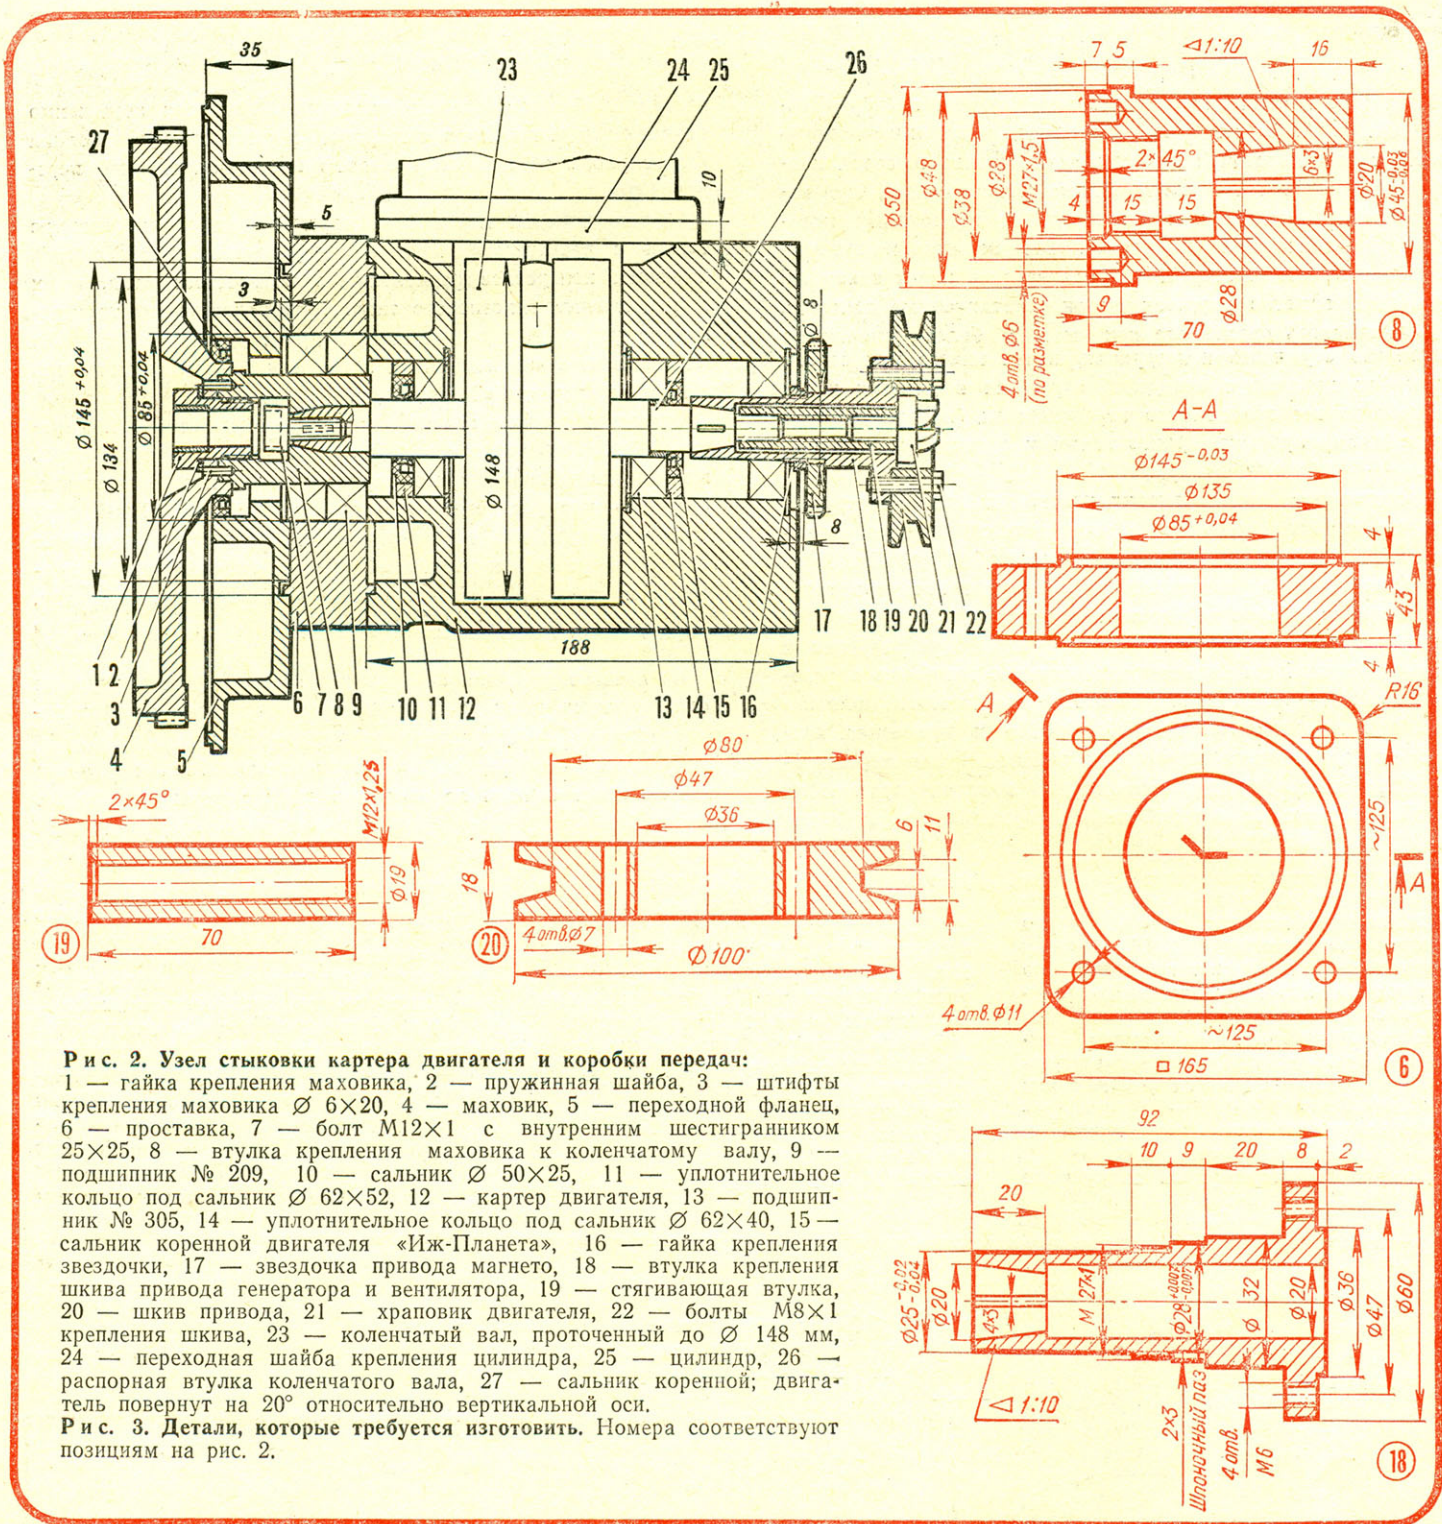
Узел стыковки картера двигателя и коробки передач:
